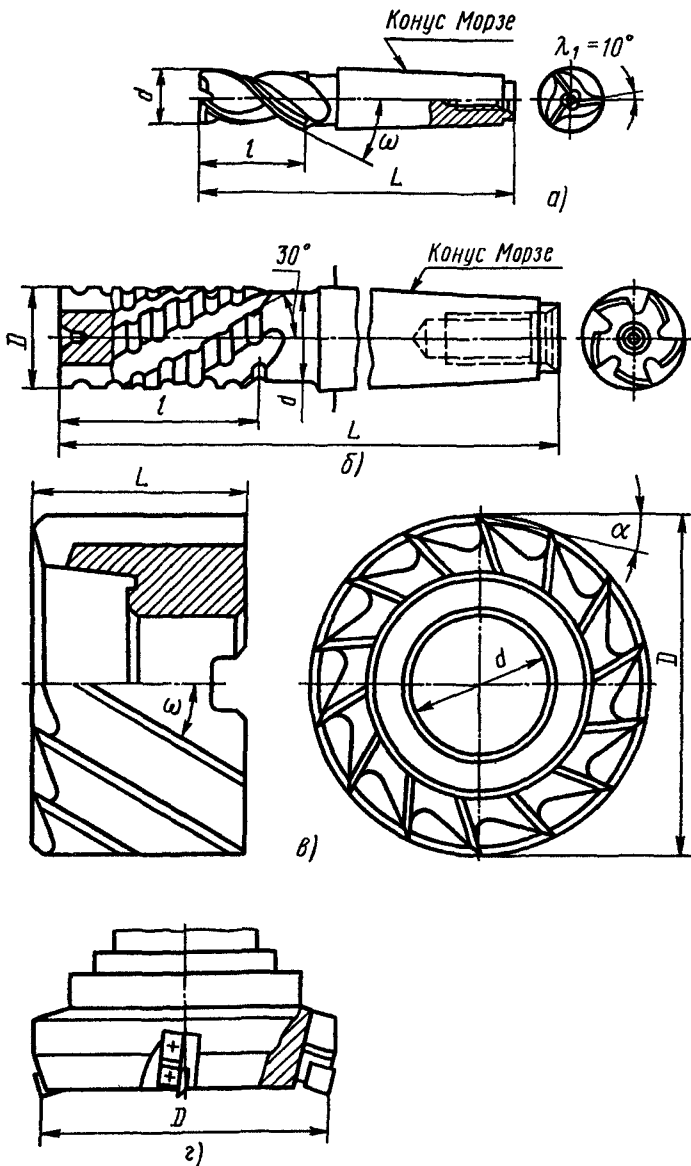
Конструкции фрез для торцевого фрезерования:
